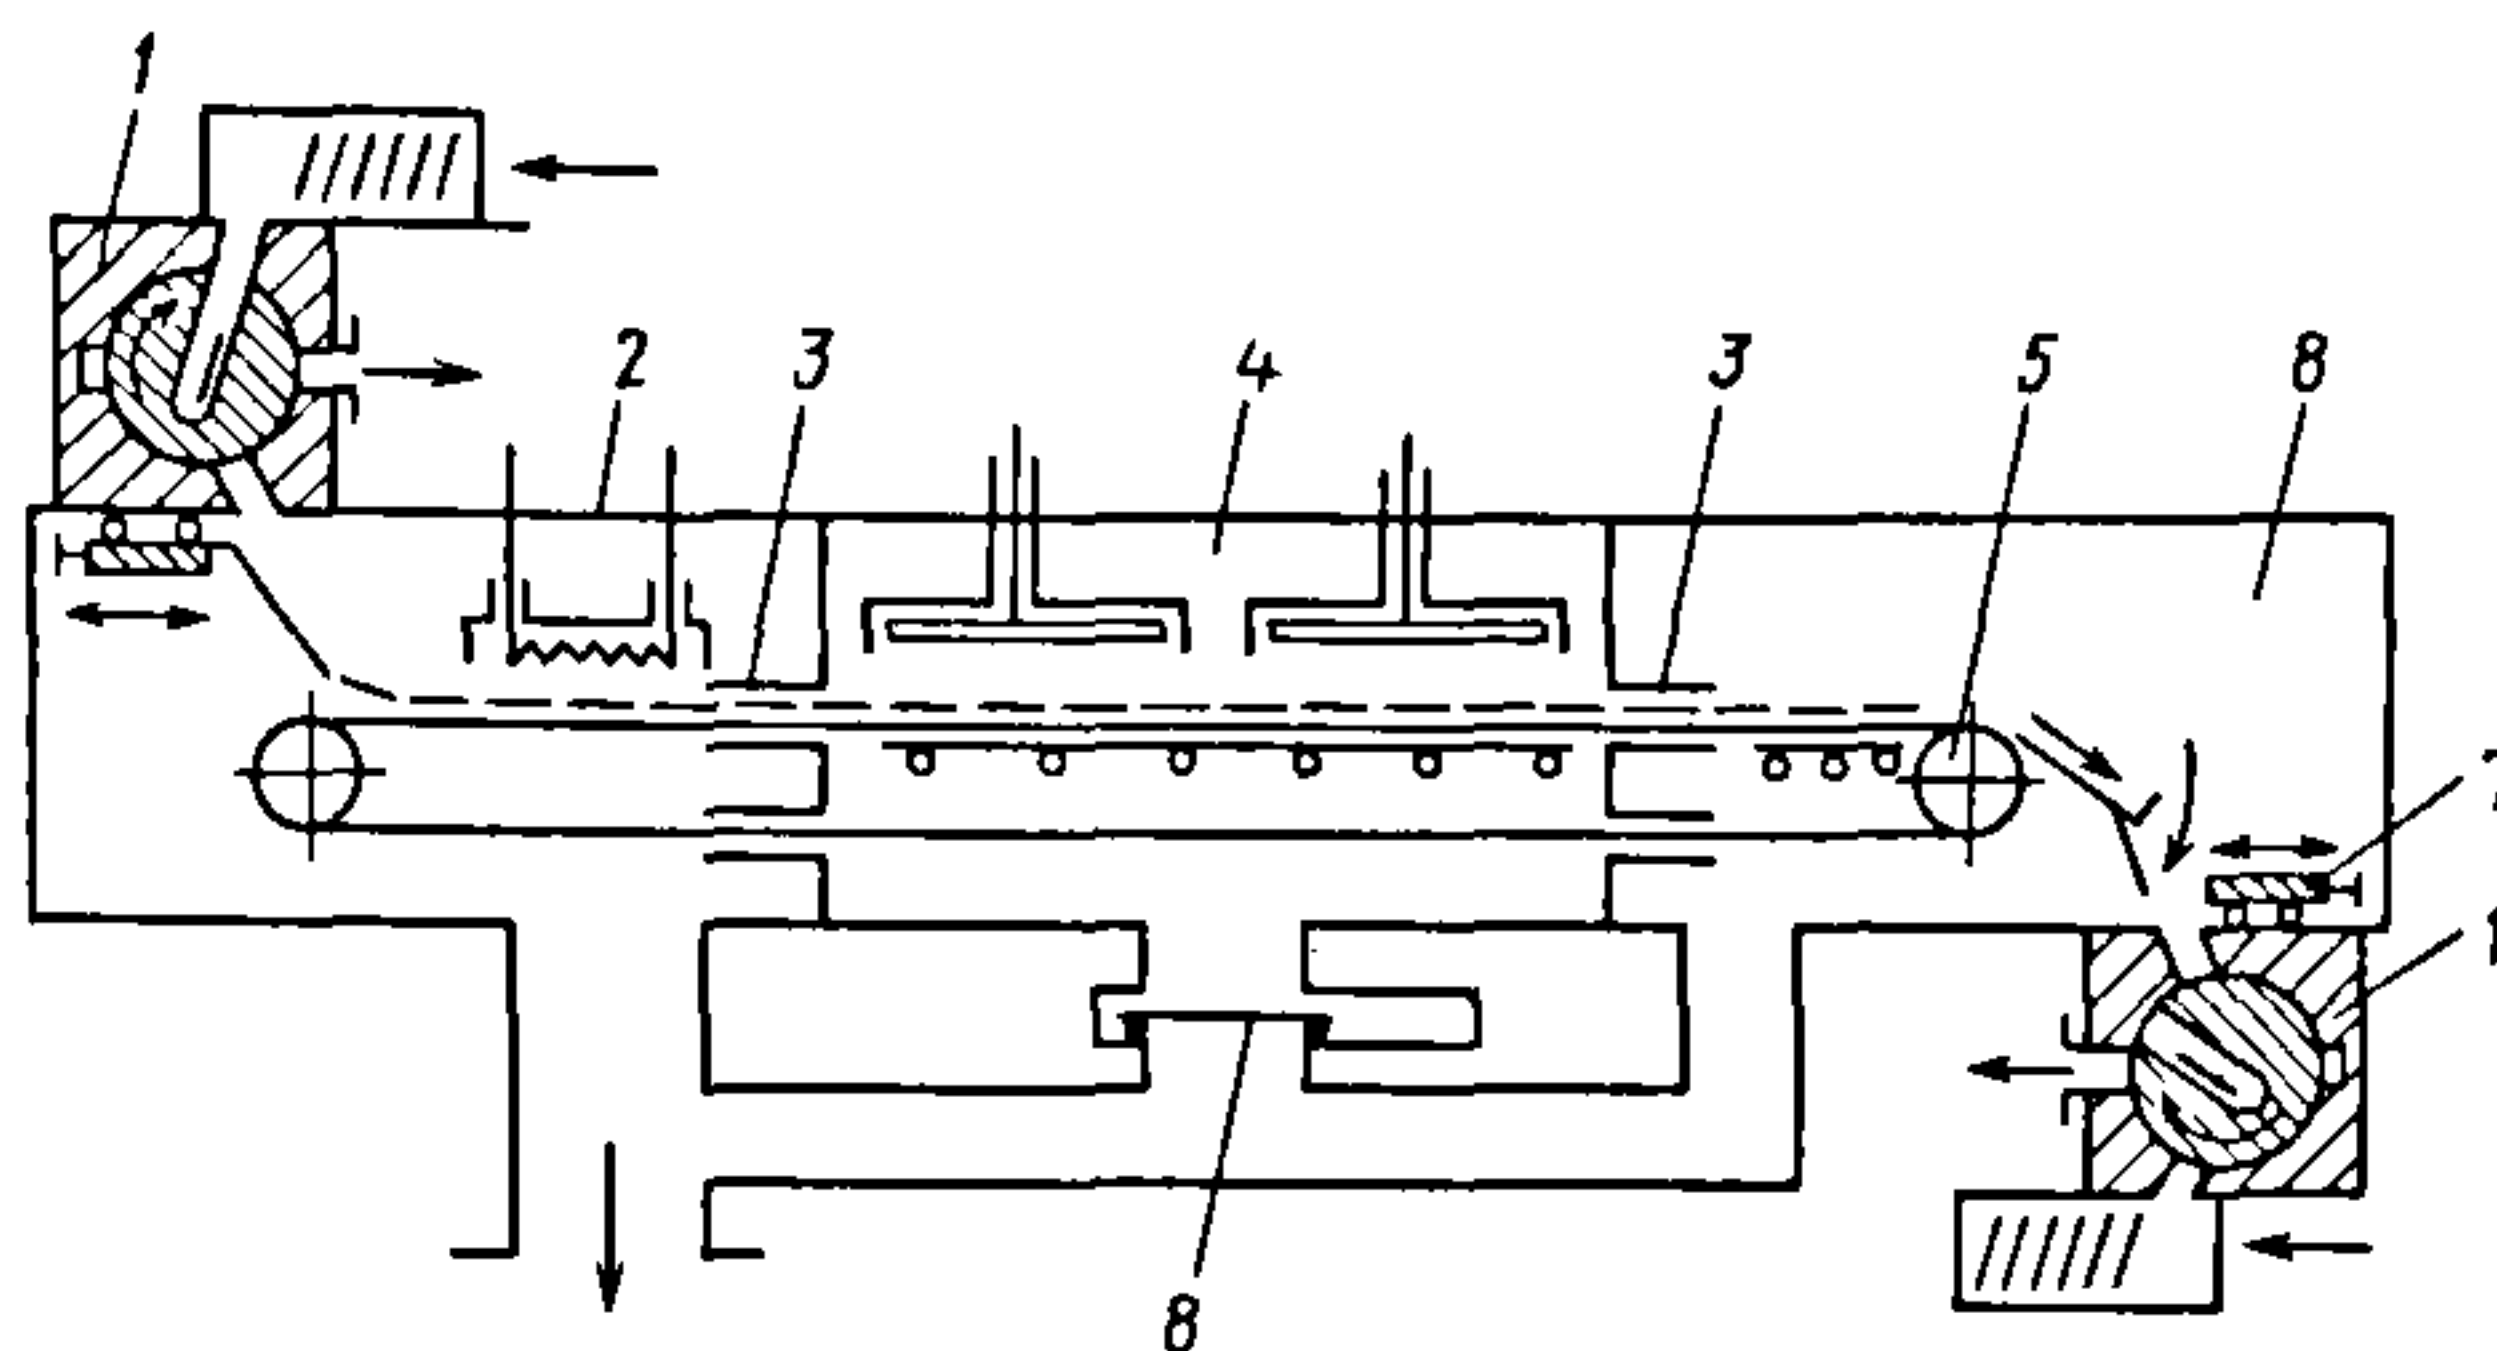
Установка непрерывного действия со шлюзовыми загрузочными устройствами:
